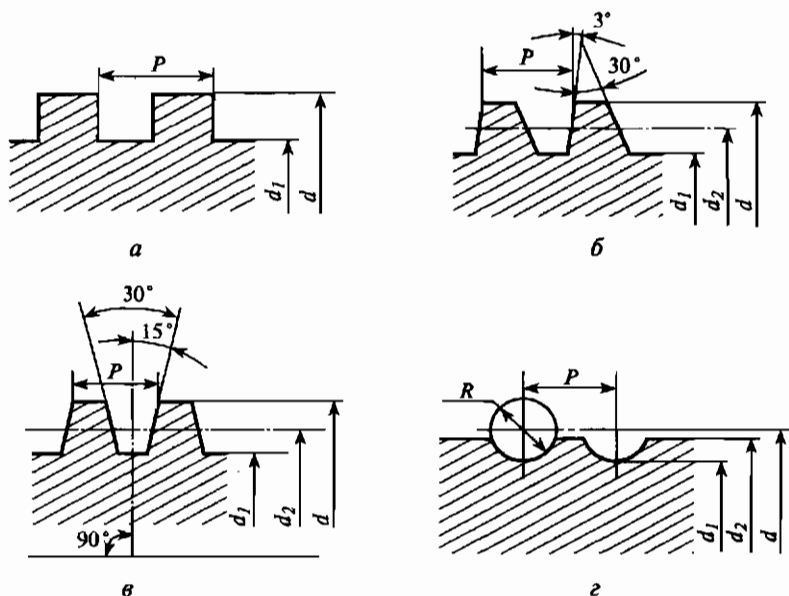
Винтовые резьбы различных профилей в передачах «винт — гайка» скольжения (ВГС) и «винт — гайка» качения (ВГК):
